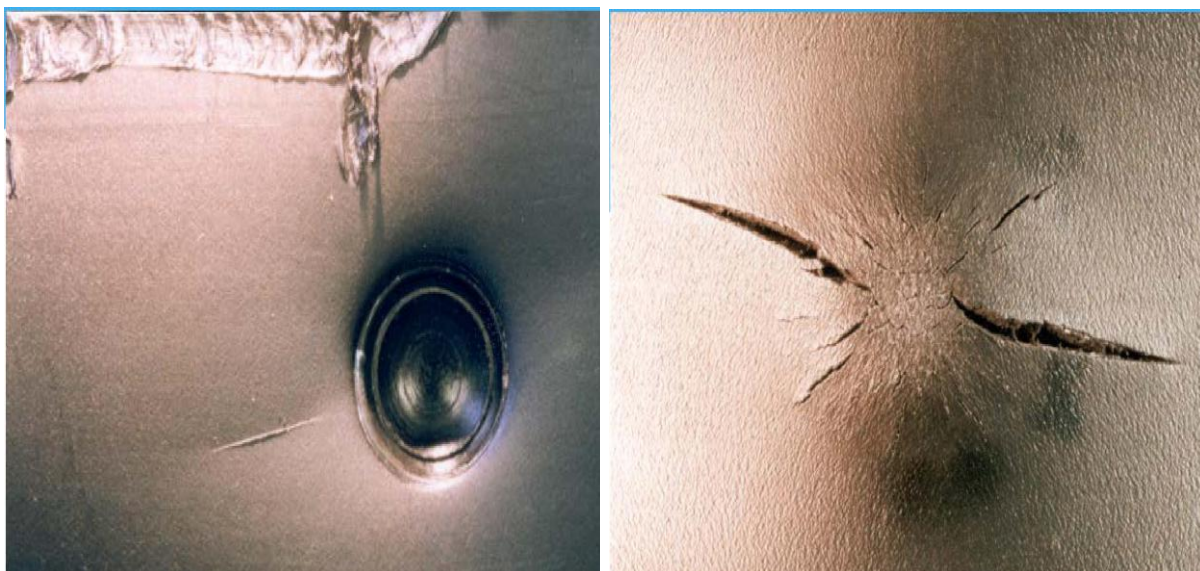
Испытание точечной нагрузкой трубы со сплошной стенкой
